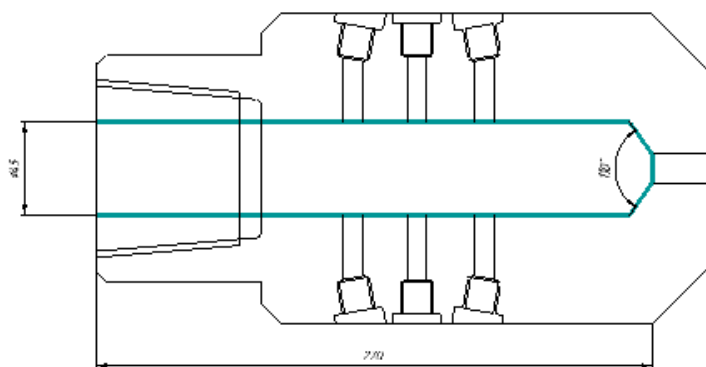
Схема базирования заготовки при сверлении отверстия $\varnothing 45 \text{ Н}8^{(+0,072)}$ мм.
